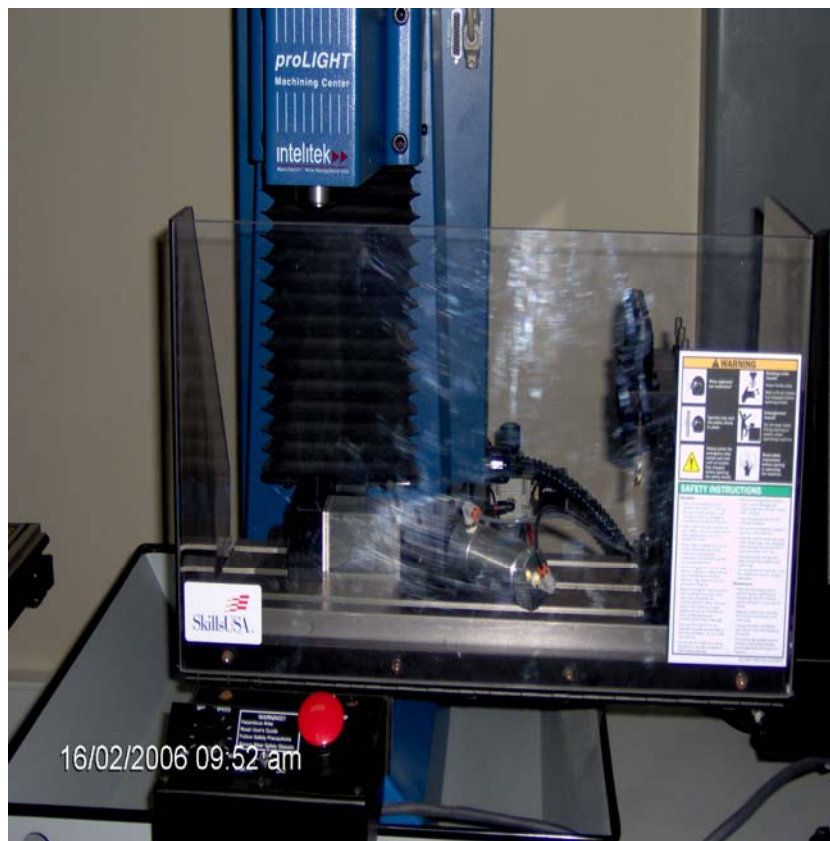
Vista frontal de Fresadora CNC Pro Light 1000 de Intelitek
